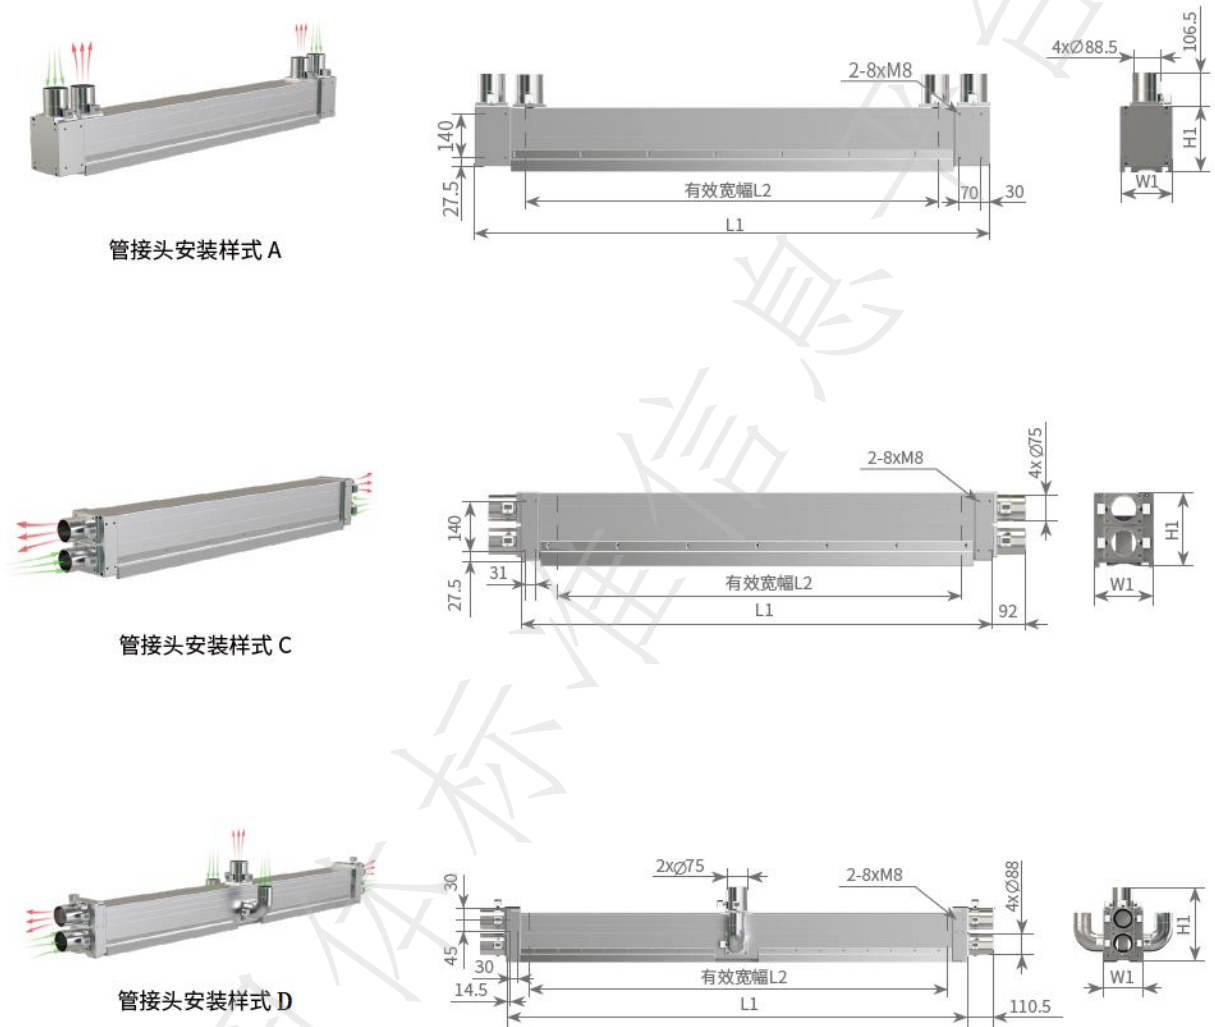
UWL 型（适用于材料幅宽在 1100~1800 mm 的场景）安装尺寸图
